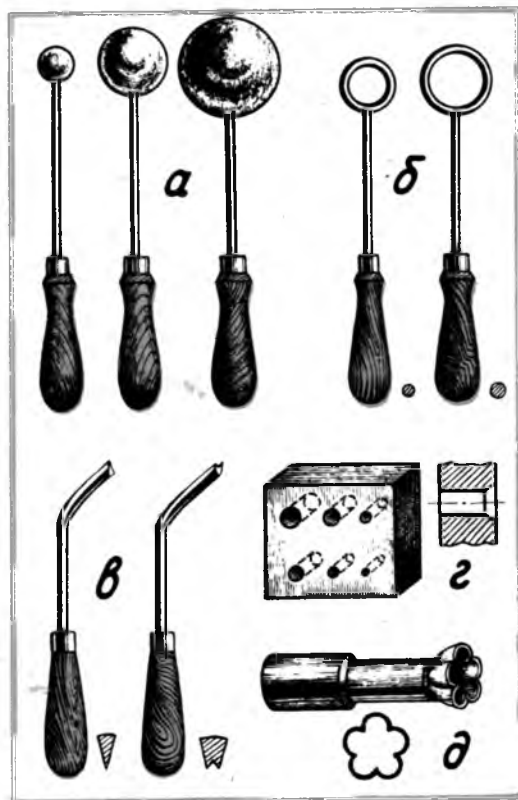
Инструменты для изготовления цветов: а — бульки; б — кольца; в — ножи; г — утюжок; д — высечка
